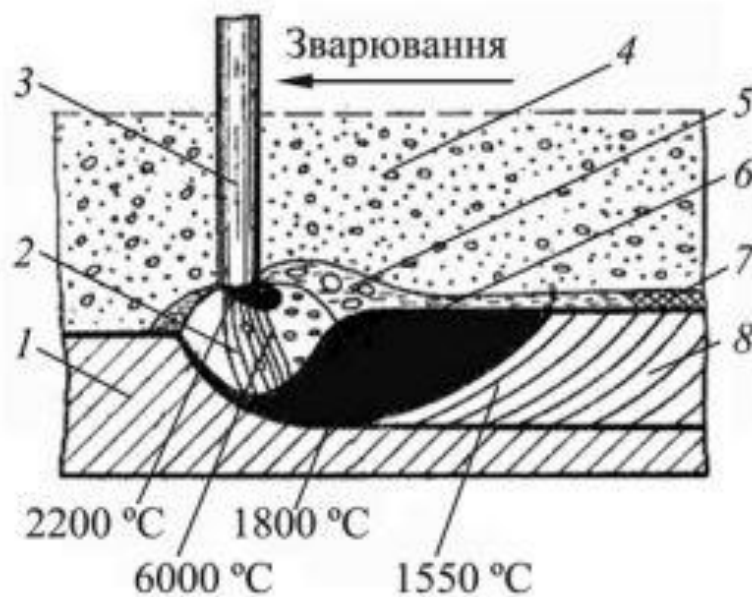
Схема процесу електродугового зварювання під шаром флюсу
